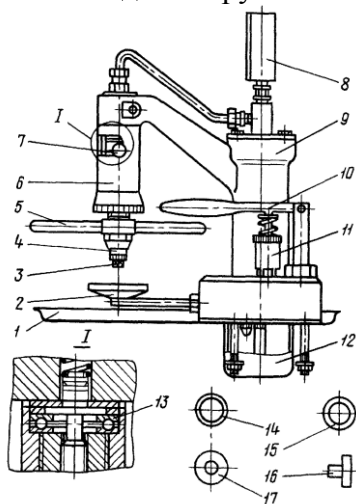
Прилад для випробовування нагнітальних клапанів: 1 – піддон; 2 - лоток зливний; 3 – тріщотка; 4 - головка мікрогвинта; 5 – вороток; 6 - механізм затиску; 7 – ручка; 8 – манометр; 9 – корпус; 10 - ручка насоса; 11 – ручний насос; 12 – бачок; 13 – підшипник; 14,15 – кільця; 16 – заглушка; 17 – прокладка.
